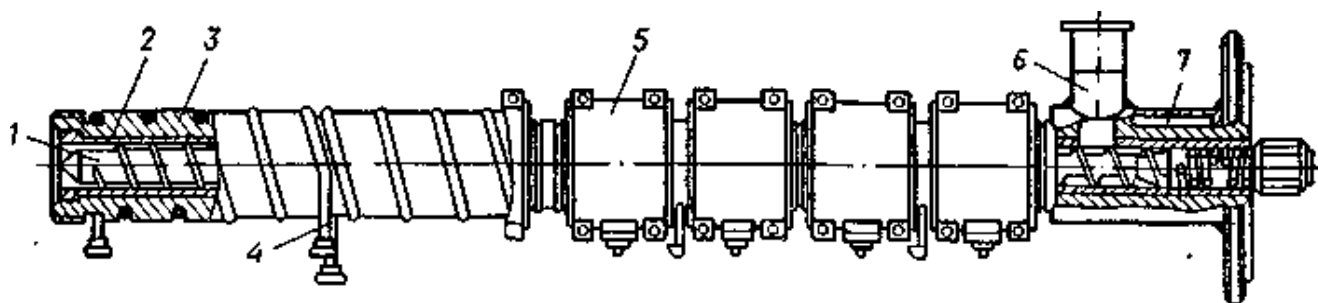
Циліндр одночерв'ячного пресу:
